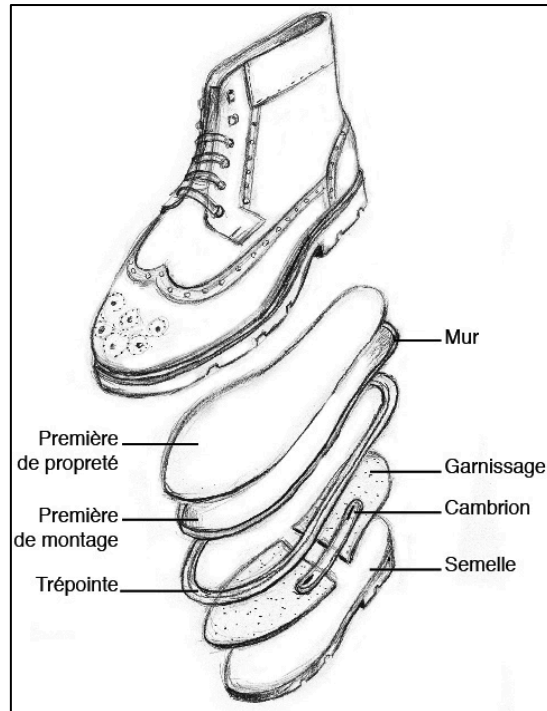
Éléments composants le semelage d'une chaussure [37]
